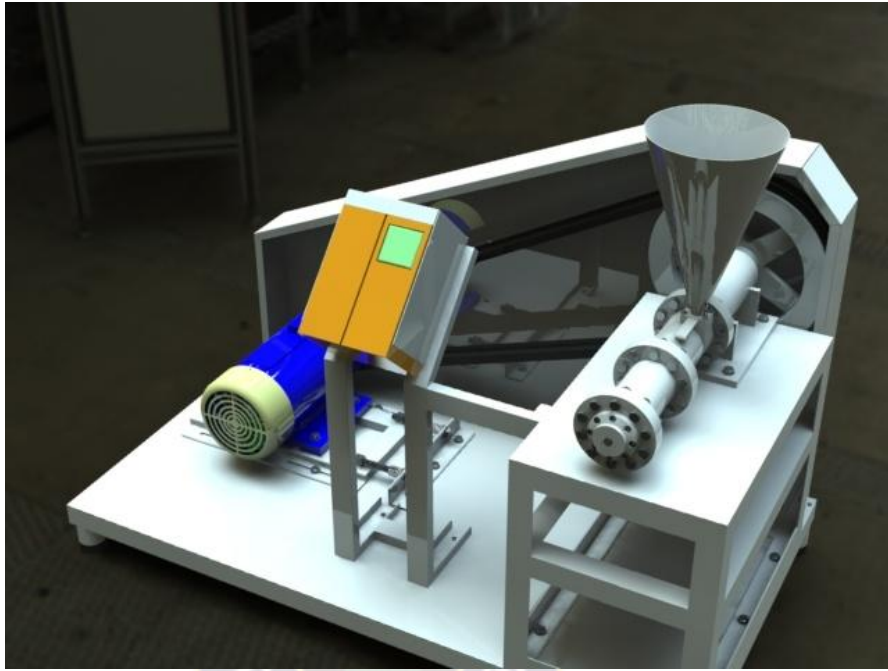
Diseño final del prototipo de extrusor en 3D.
